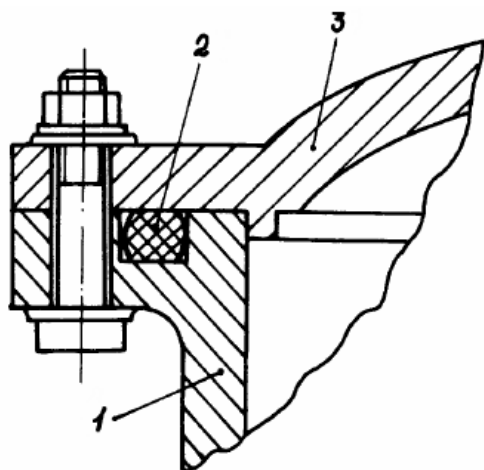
Вузол з додатковим самоущільненням фланцевого з'єднання герметизованого корпусу: 1 – корпус; 2 - герметизуюча прокладка; 3 – фланець
